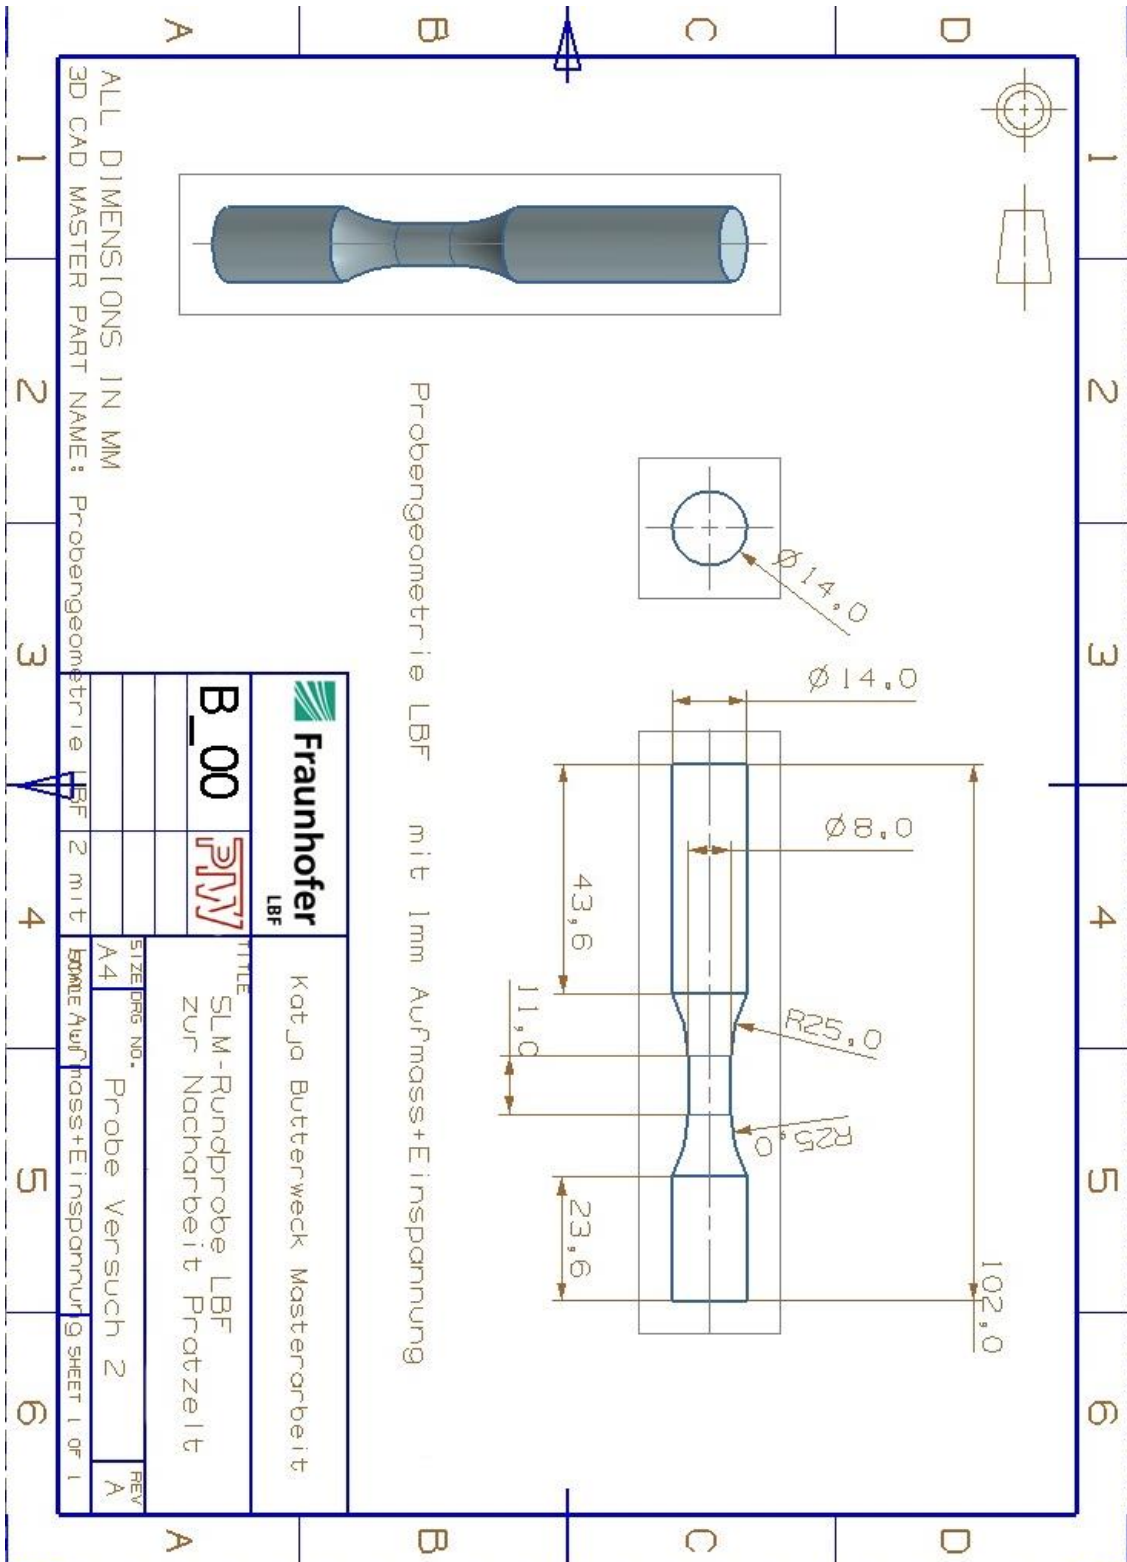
Technische Zeichnung Probengeometrie B_00
